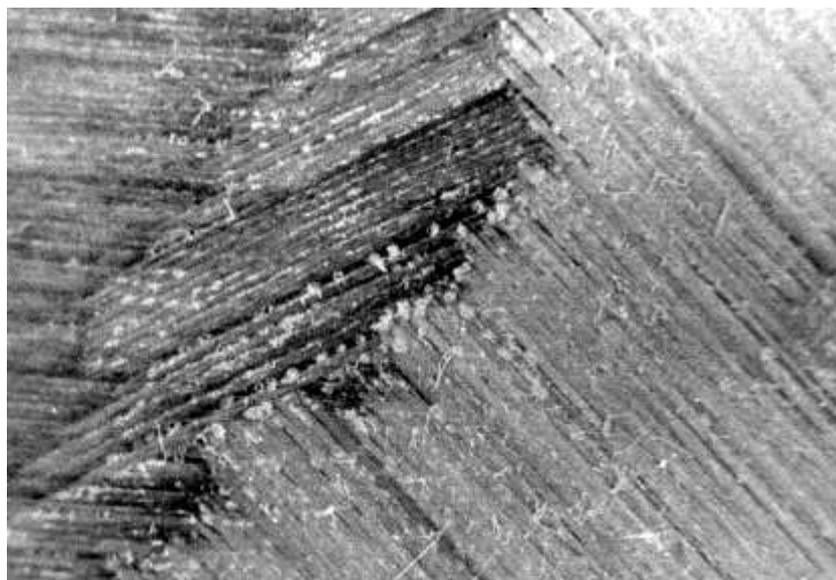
Вид поверхности изделия из органопластика СВМ-6 после токарной обработки с ДТП
